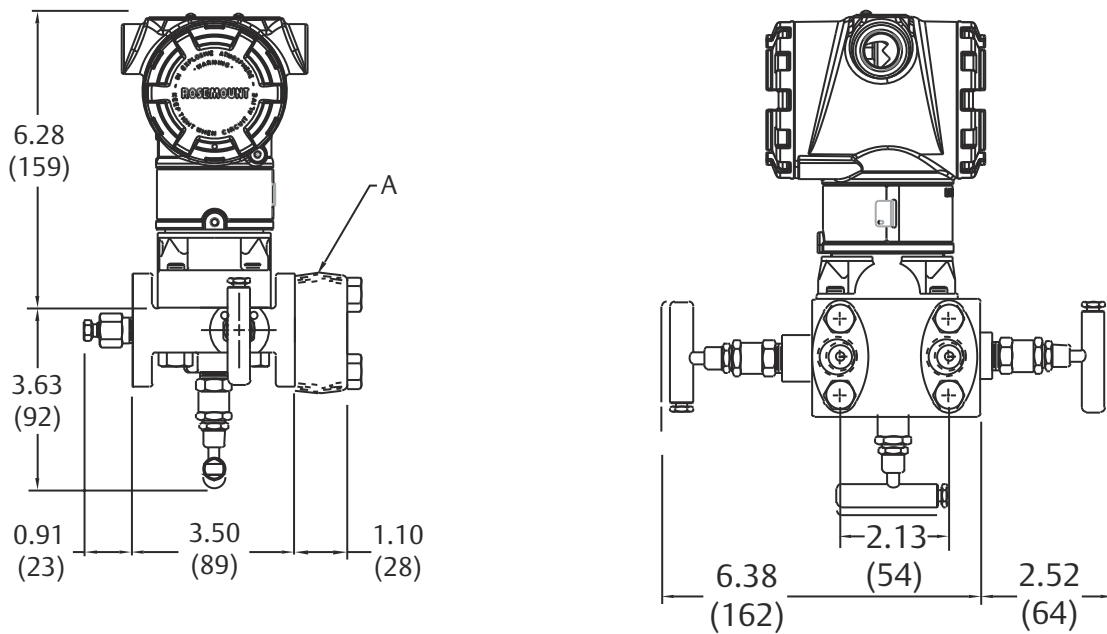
Coplanar 3051C Rosemount com flange tradicional
